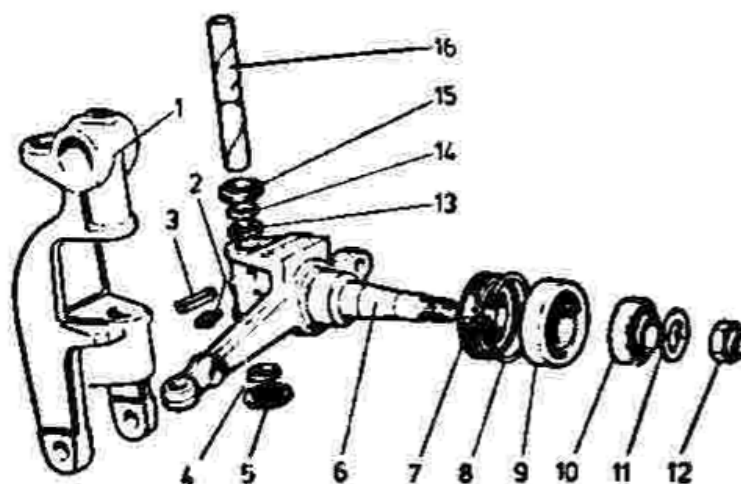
Detailní rozkreslení zavěšení předního kola
